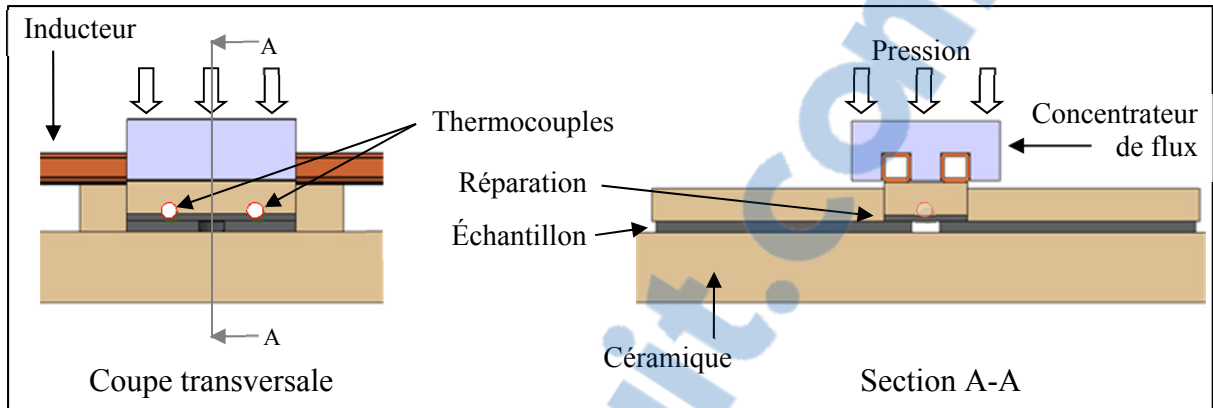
Schéma du montage pour le soudage d'une réparation simple
